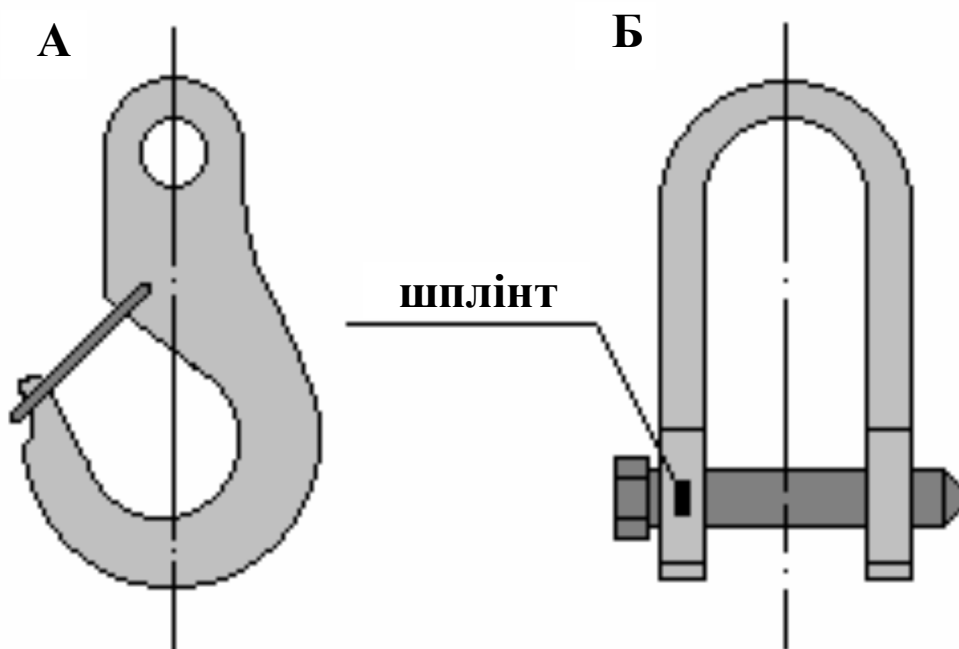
Захвати: а – причалювальний гак; б – такелажна петля
